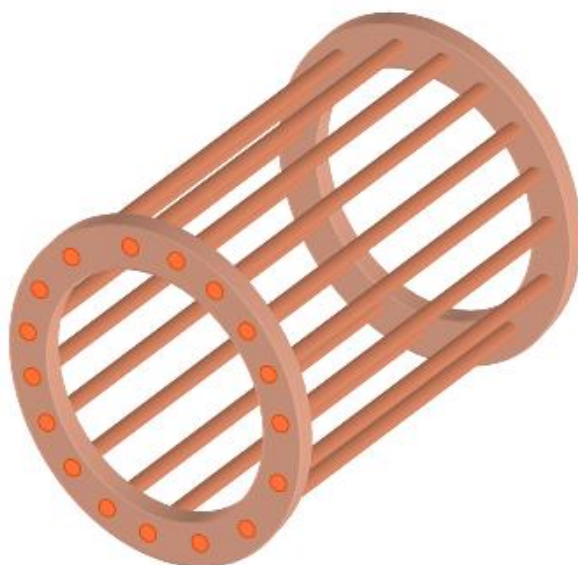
Сварная медная кз-обмотка ротора асинхронного двигателя
